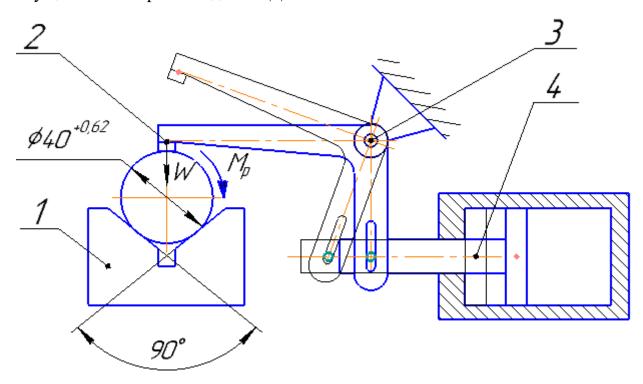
Кинематическая схема гидравлического зажима: $1 - \Pi$ ризма; 2 -рычаг; 3 -ось; 4 -гидроцилиндр; Д -деталь.
